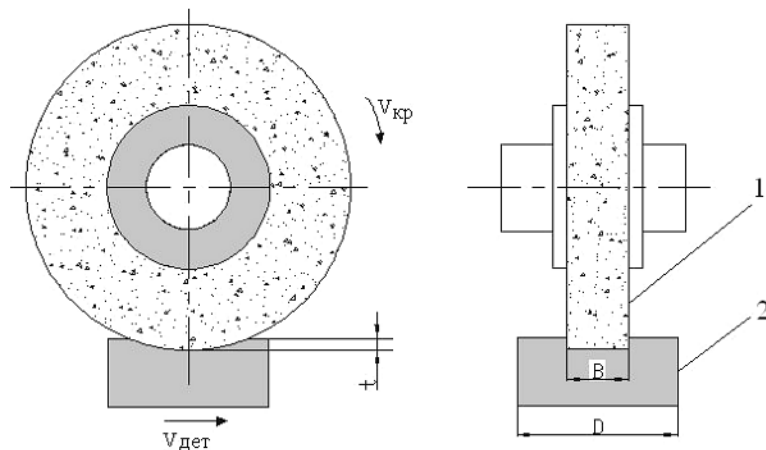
Процес плоского шліфування периферією шліфувального круга: 1 – циліндричний шліфувальний круг; 2 – заготовка [28]
